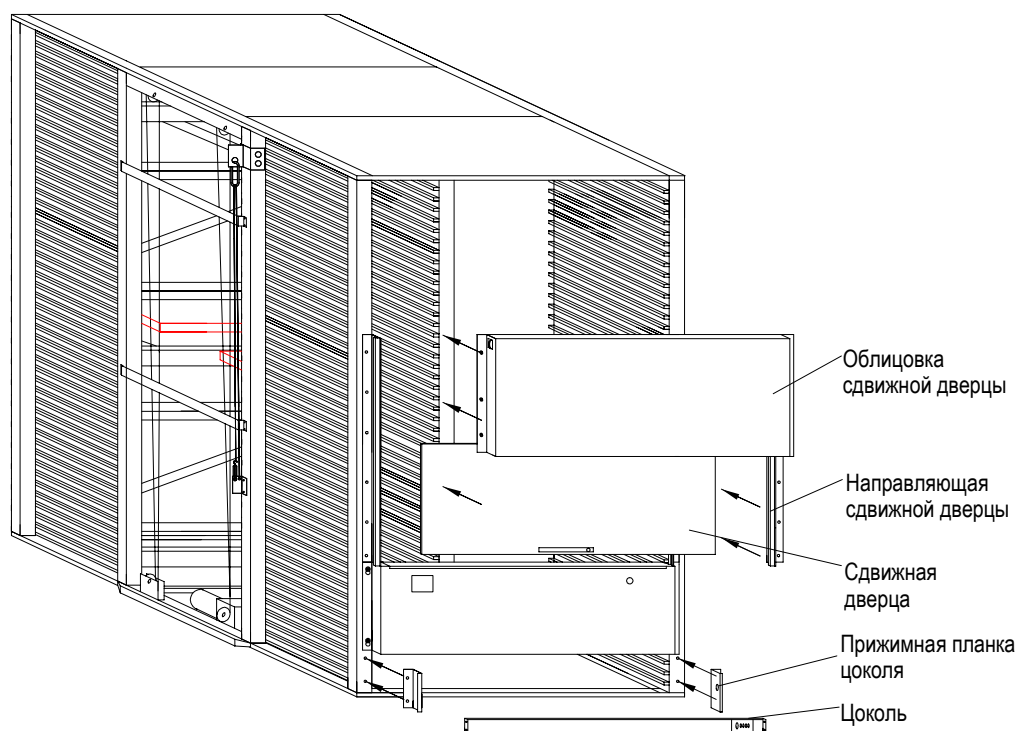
Монтаж передних стенок и сдвижной дверцы
